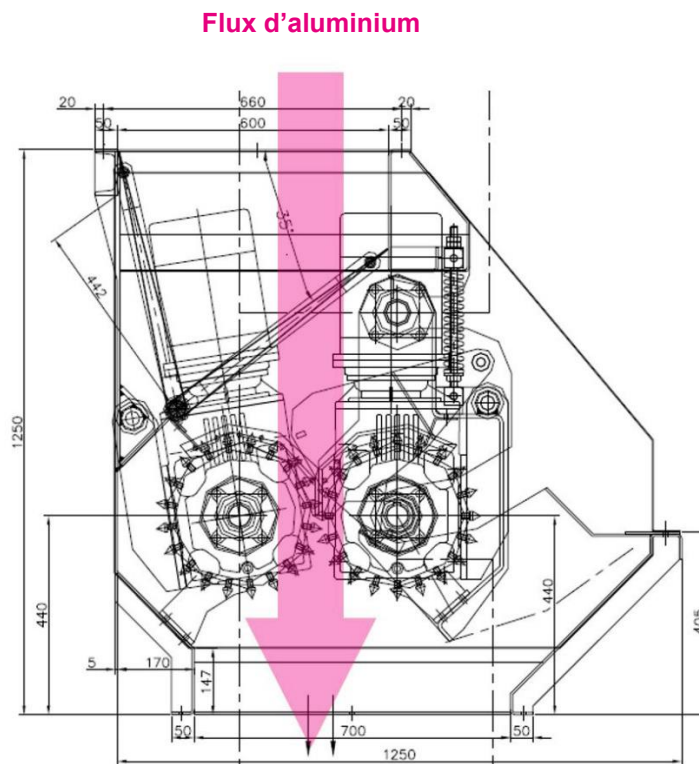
Vue latérale du pré-conditionneur d'aluminium
